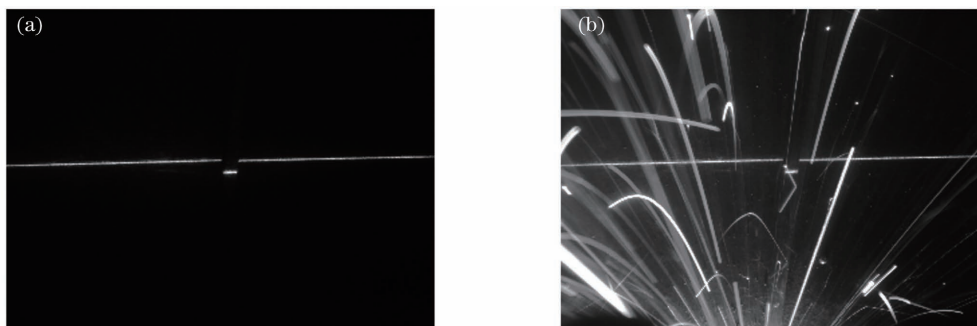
焊接前和焊接过程中的焊缝图像。(a)焊接前;(b)焊接过程中
